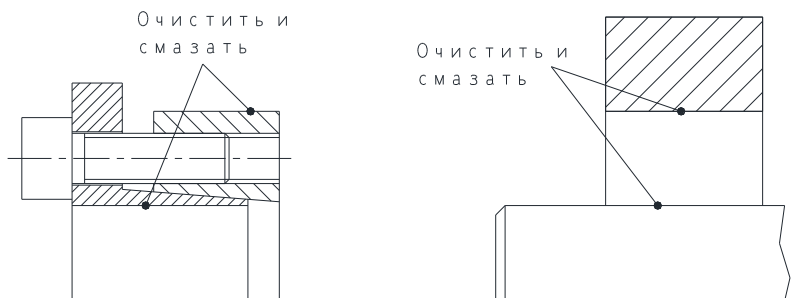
Чистка и смазка поверхностей (пример: CLAMPEX® KTR 206)
